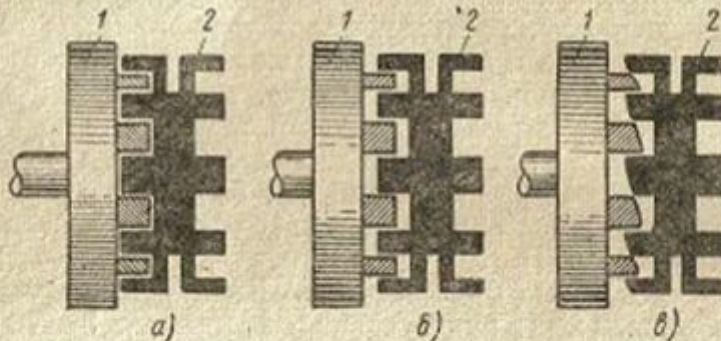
Зацепление кулачков шестерни и муфты включения коробки передач:
